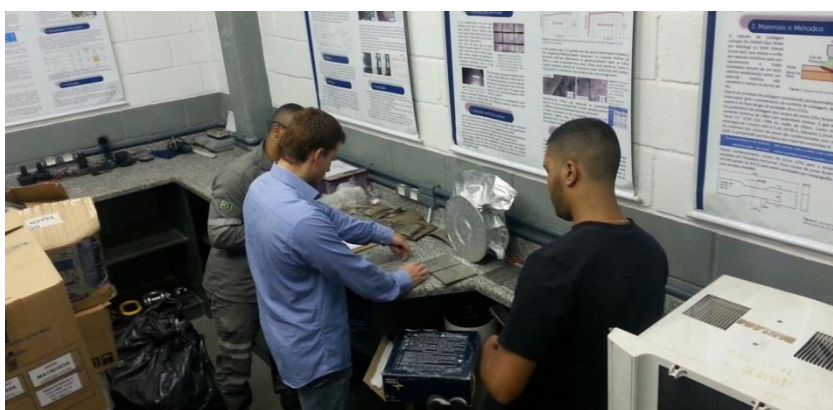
Inspetor de soldagem orientando para realização da soldagem dos materiais.
